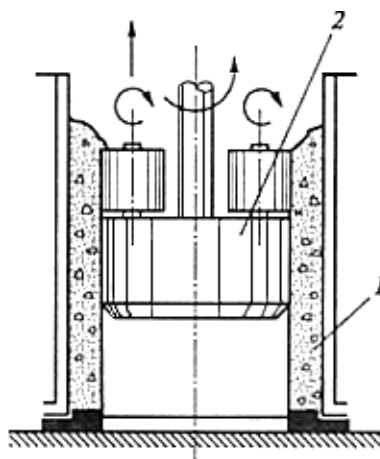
Изготовление полых свай методом радиального прессования: 1 — стенка свай; 2 — роликовая головка
